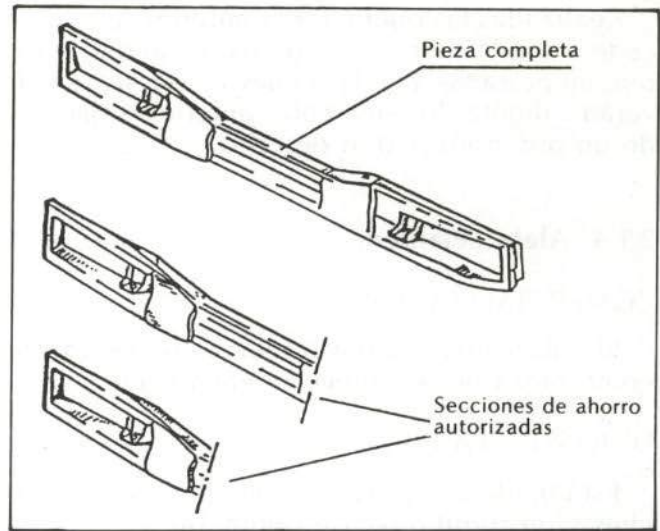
Recambio y secciones de ahorro de la traviesa inferior.
